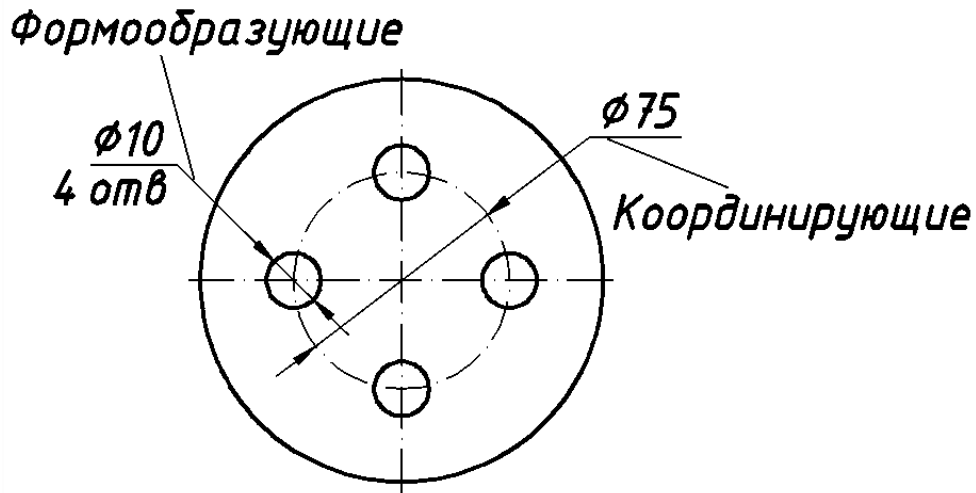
Образец нанесения координирующих и формообразующих размеров.
